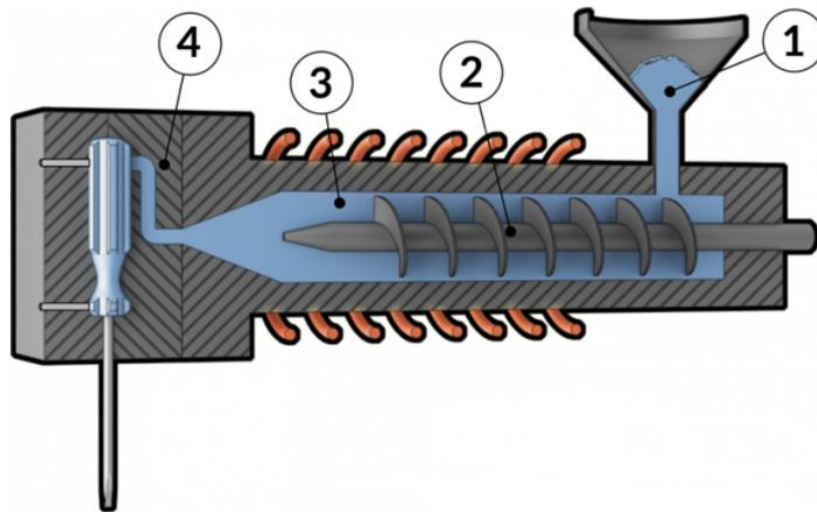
Esquema do processo de moldação por insertos (adaptado de [7])
